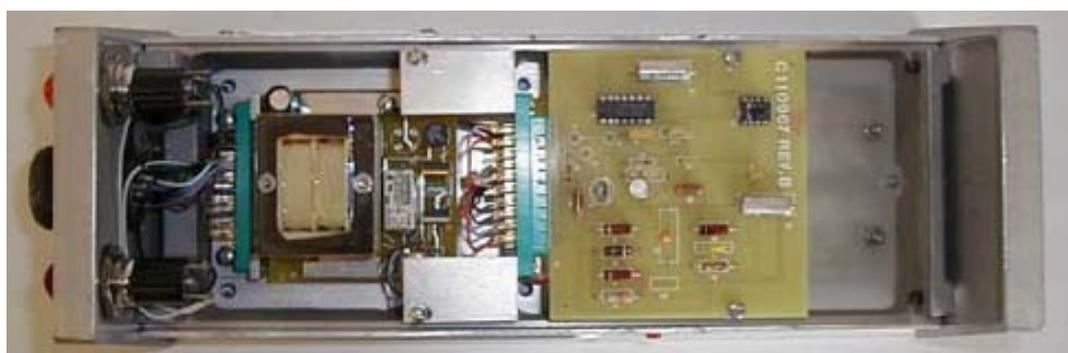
Vista superiore assemblaggio Rilevatore giunte
